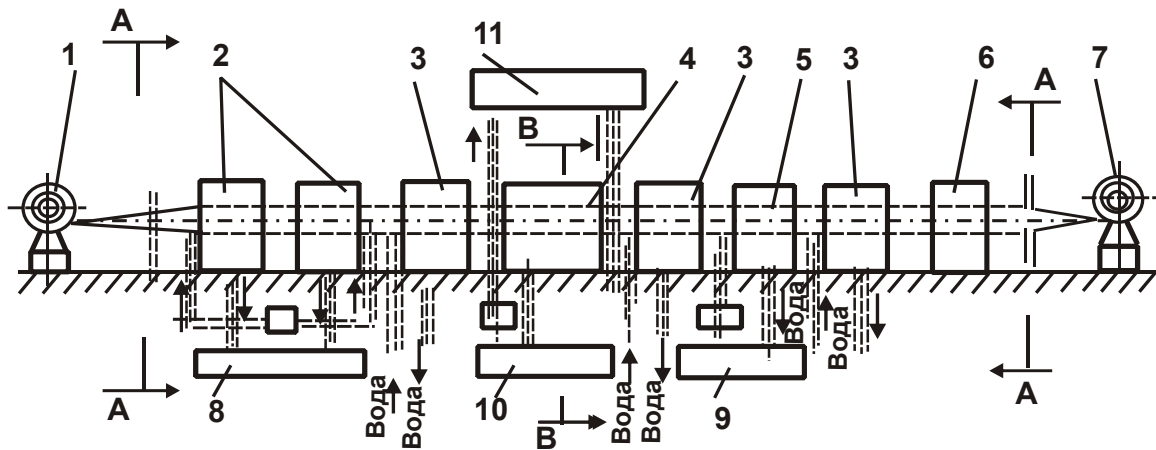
Схема установки для електрохімічного полірування трубчастих елементів зі стрічок
